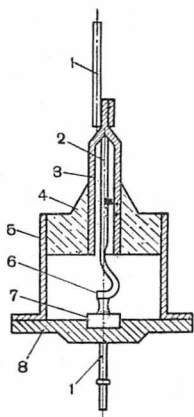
Конструкция плоскостного диода: 1 — наружный вывод; 2 — внутренний вывод; 3 — трубка; 4 — изолятор; 5 — корпус; 6 — электрод; 7 — кристалл германия; 8 — кристаллодержатель
